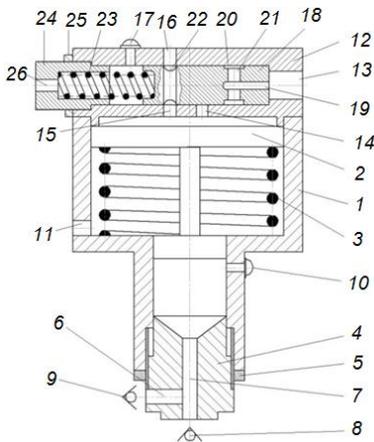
Устройство для автоматического ввода депрессорной присадки:
